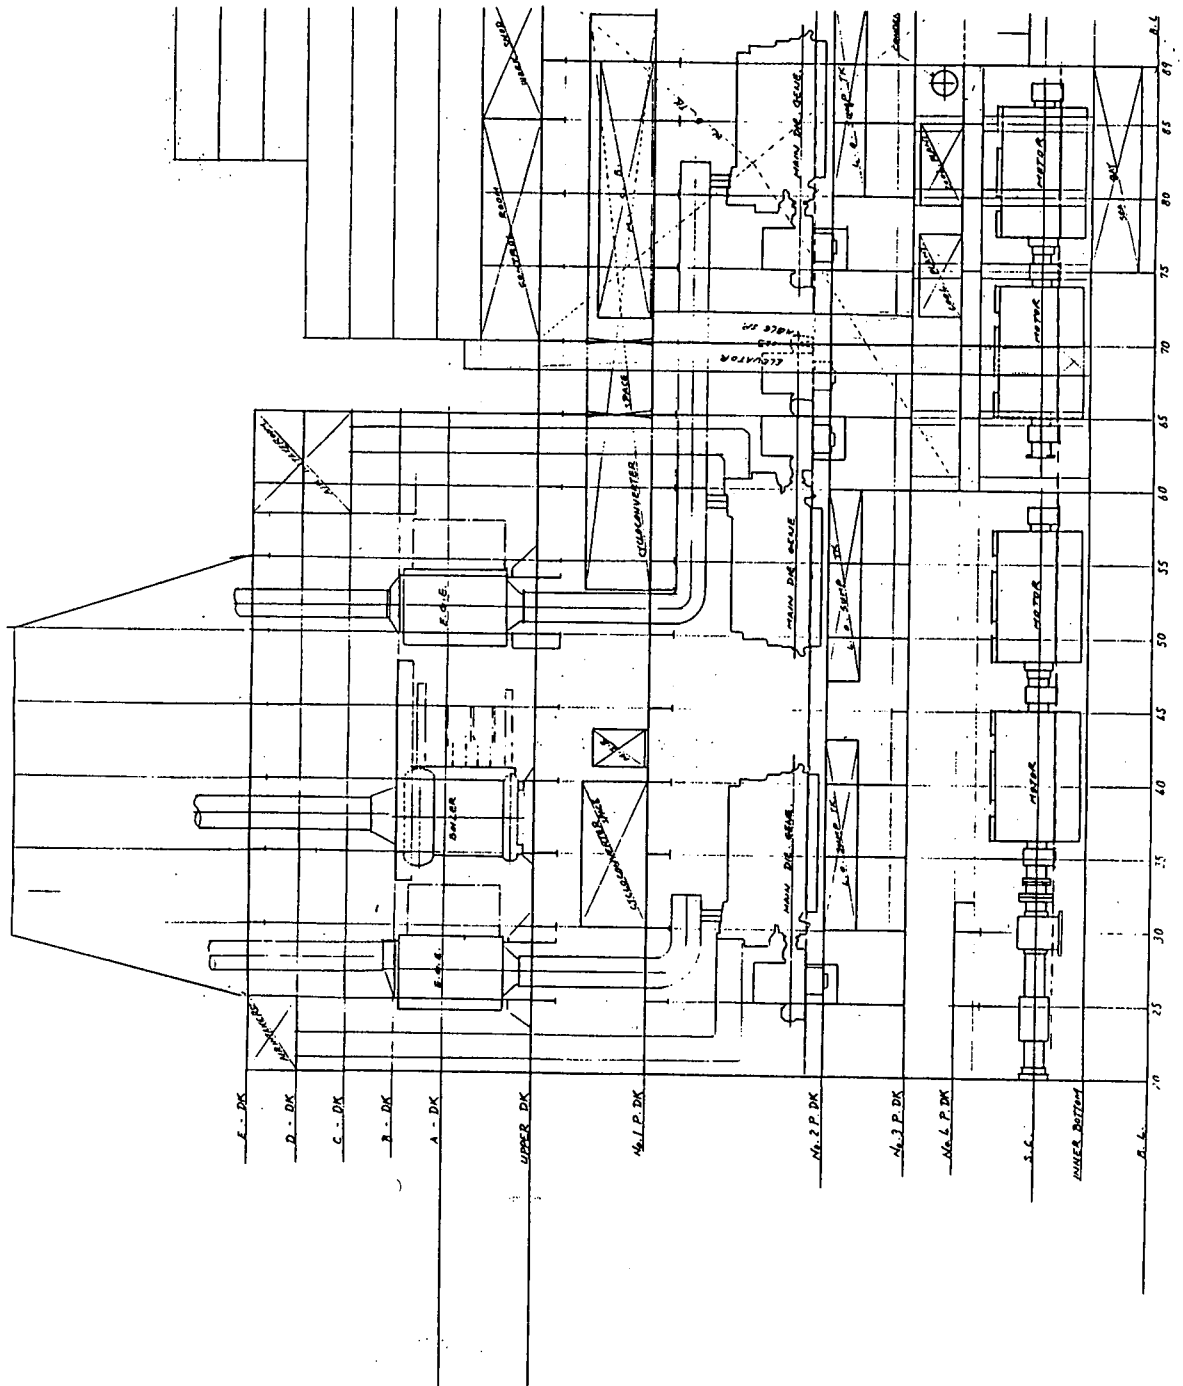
E 方式 ELEVATION(PORT SIDE)
